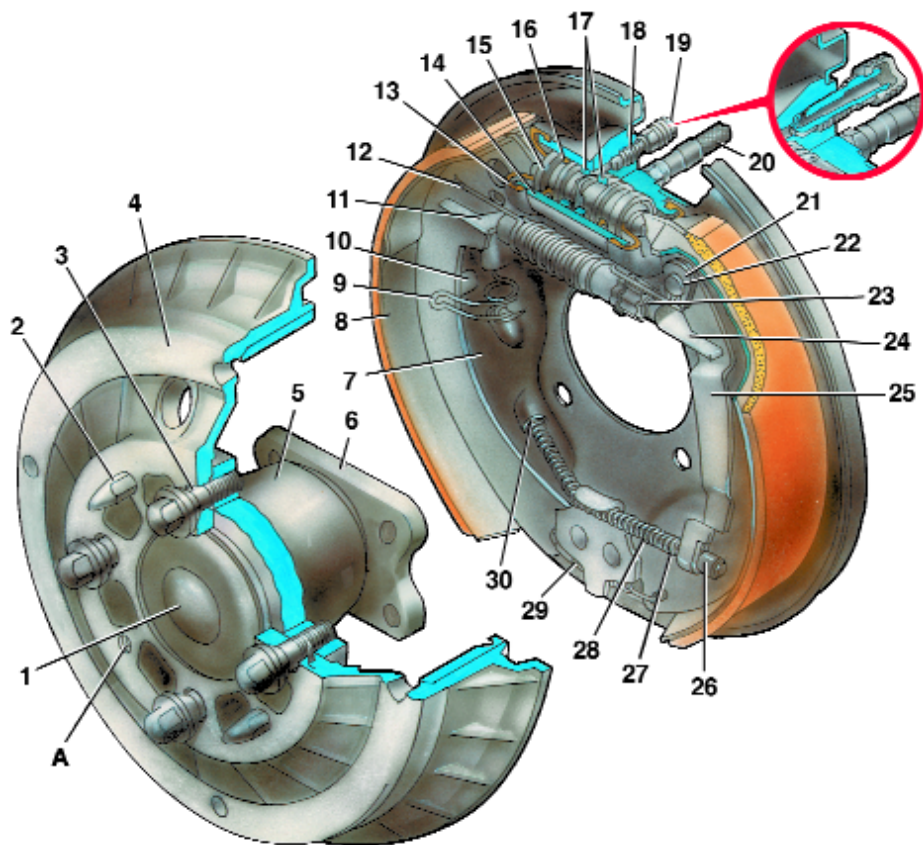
Тормозные механизмы задних колес: 1 – колпачок; 2 – фиксатор; 3 – болт крепления колеса; 4 – тормозной барабан; 5 – ступица; 6 – цапфа; 7 – щит тормоза; 8 – тормозная колодка; 9 – прижимная пружина; 10 – упор; 11 – наконечник распорной планки (длинный); 12 – стяжная пружина (длинная); 13 – грязезащитный чехол; 14 – цилиндр; 15 – поршень; 16 – манжета; 17 – упорные кольца; 18 – клапан выпуска воздуха; 19 – колпачок клапана; 20 – гибкий шланг; 21 – замковая шайба; 22 – ось; 23 – регулировочная гайка; 24 – наконечник распорной планки (короткий); 25 – разжимной рычаг; 26 – наконечник троса; 27 – пружина троса; 28 – трос; 29 – стяжная пружина (короткая); 30 – разрезная шайба; А – отверстия с резьбой для съема барабана
